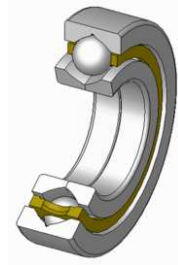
, Rodamiento de contacto angular, fuente, www.skf.com
